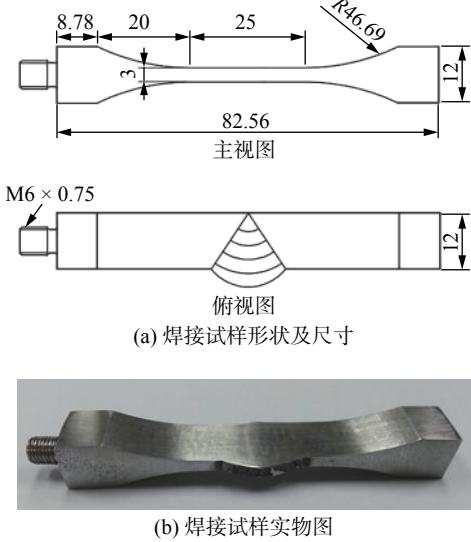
焊接接头试样形状尺寸及实物图 (mm)
